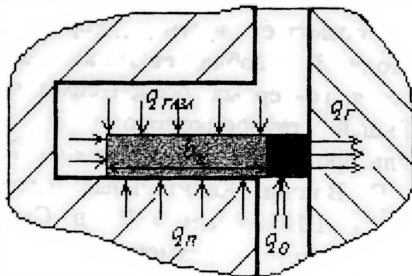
Расчетная схема тепловой нагрузки на кольцо
